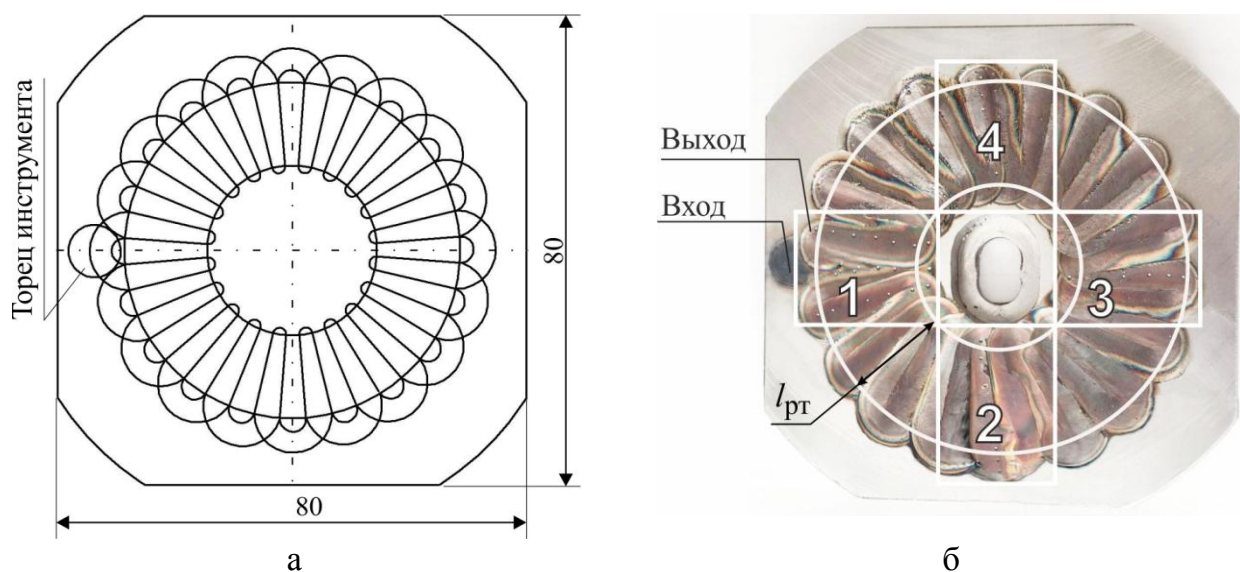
Модель верной траектории движения центра инструмента (а) и вид заготовки после ОТП по верной траектории (б)
